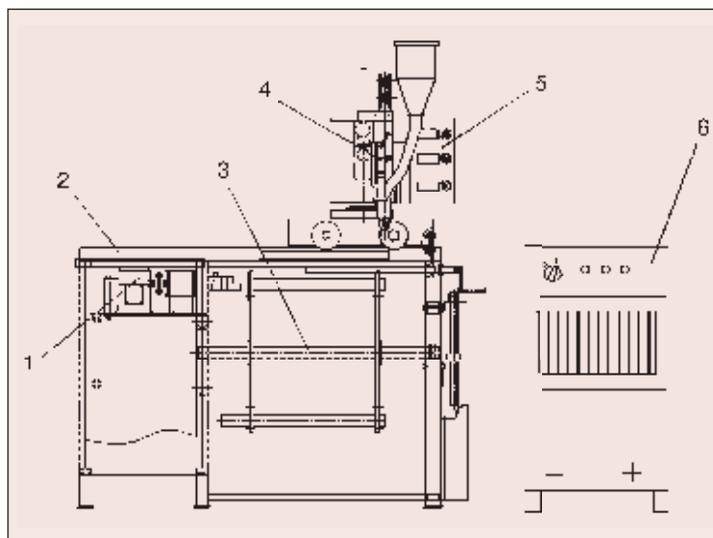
Общий вид установки: 1 — привод вращения; 2 — стол с механизмом вращения; 3 — приспособление для крепления деталей (карусель); 4 — сварочная головка; 5 — блок управления; 6 — источник питания
